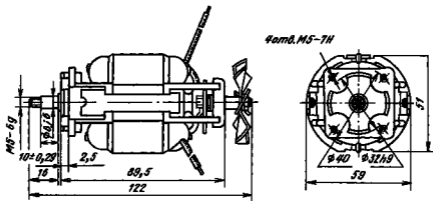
Габаритные и установочно-присоединительные размеры двигателей ДК 58-60-12
